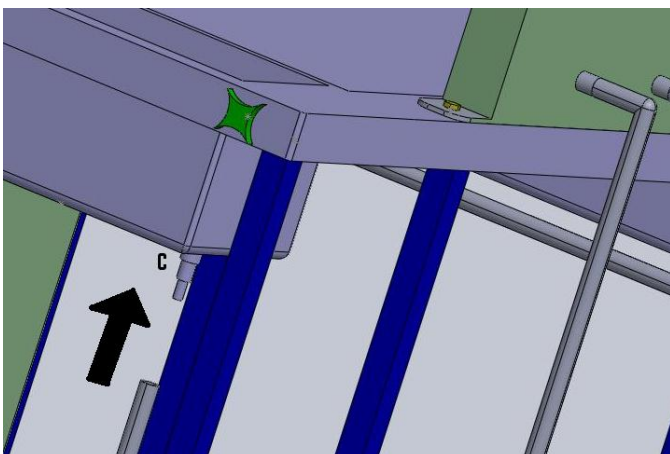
Ensamble de la tubería de desagüe en el conector C
